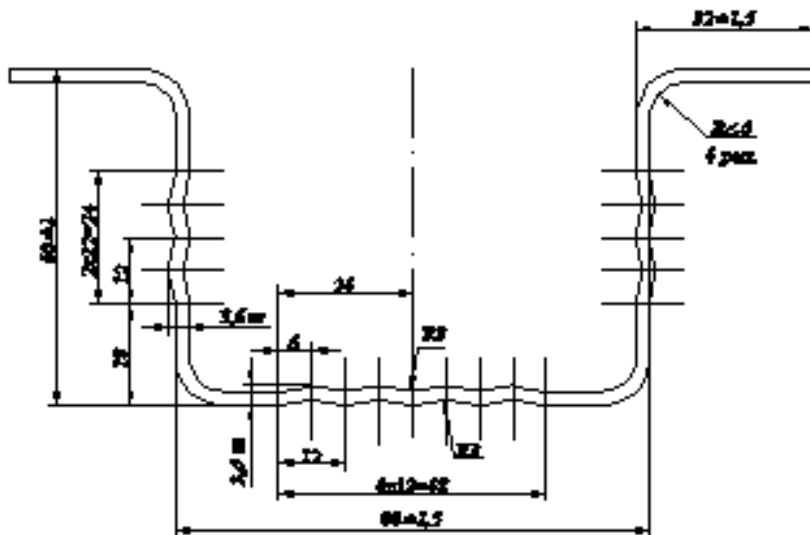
Корытный профиль 80x60x32x2,5 мм.
